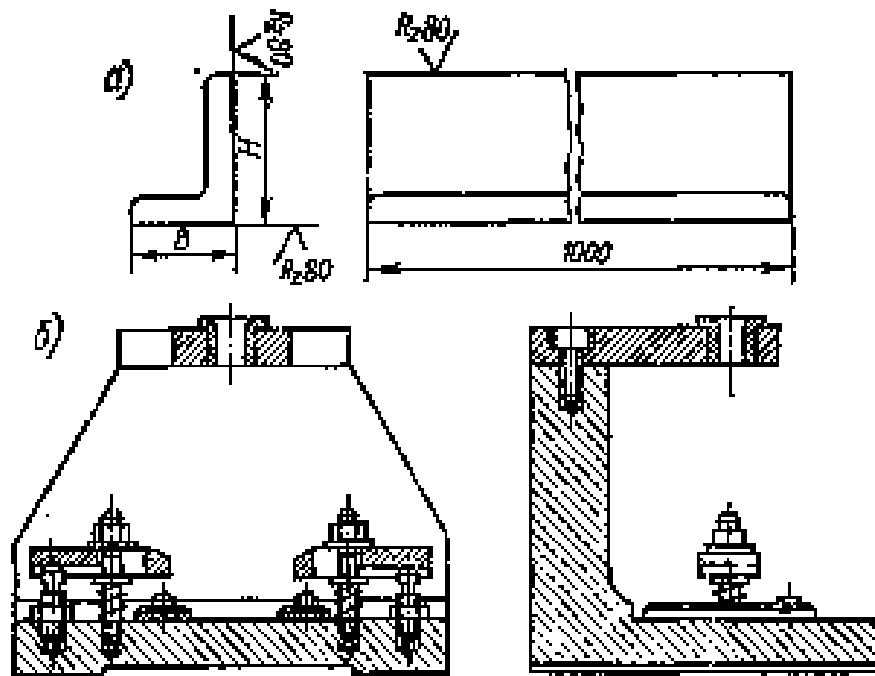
Заготовка корпуса пристрою із кутника (а) і використання його в пристрої (б)
